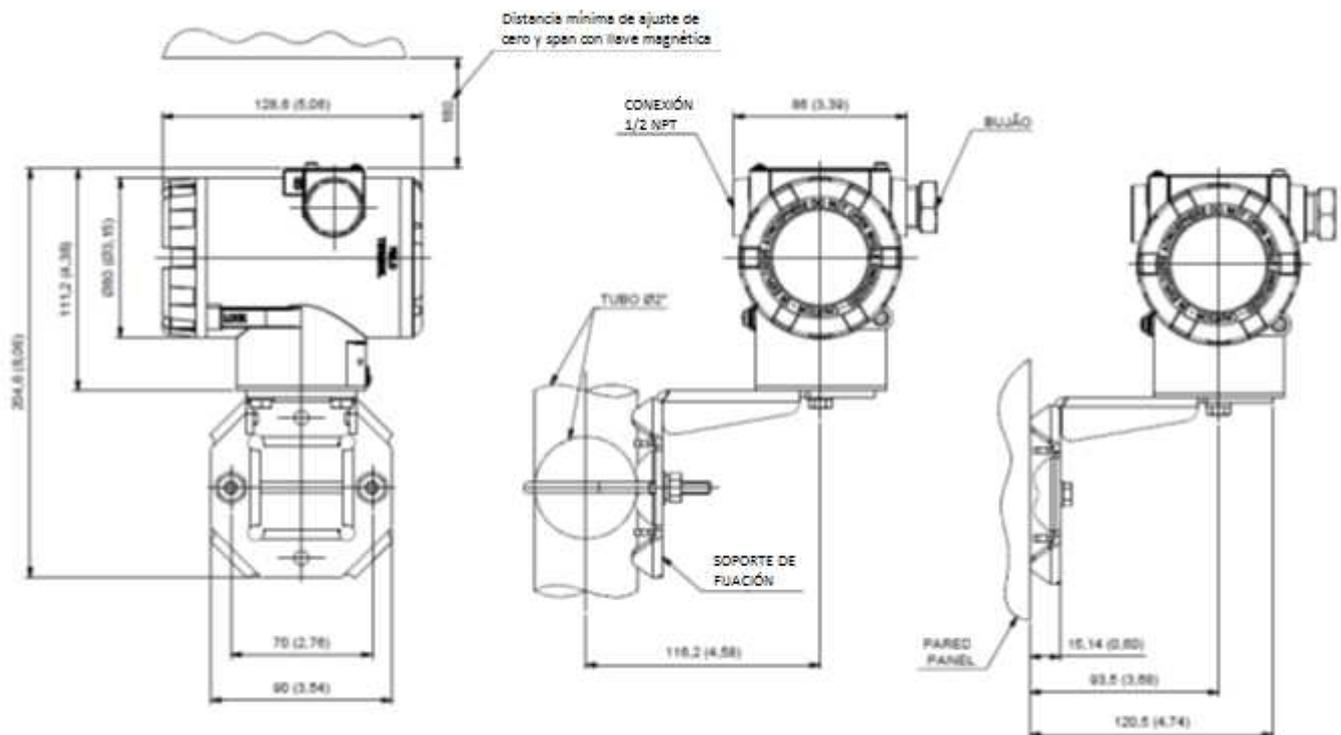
Diseño dimensional y esquema de montaje del VTT10-FH.
